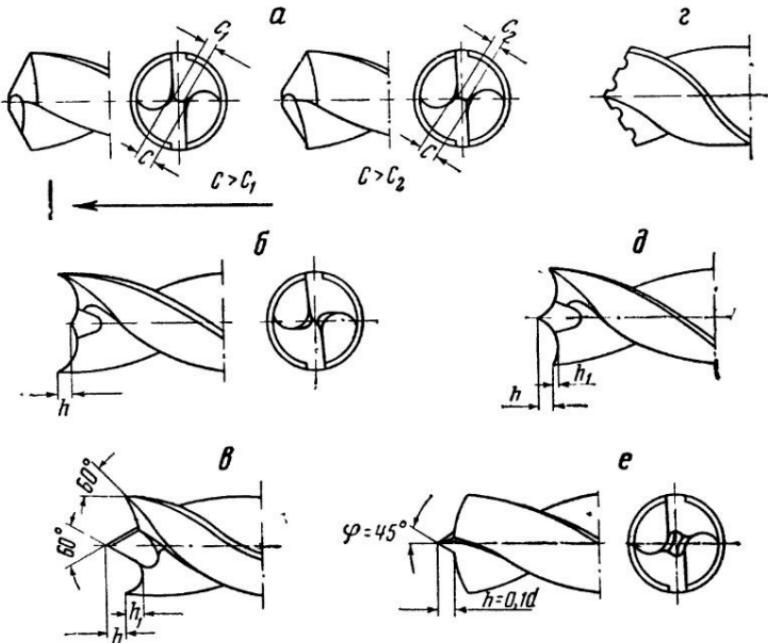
Виды заточки сверл: *а* — подточка поперечной кромки для уменьшения осевого усилия, *б*, *д* — заточка для сверления слоистой пластмассы, *в* — заточка для сверления пластмасс и мягких цветных металлов и сплавов; *г* — выточки для дробления сливной стружки; *е* — заточка для сверления листовой и полосовой стали.
